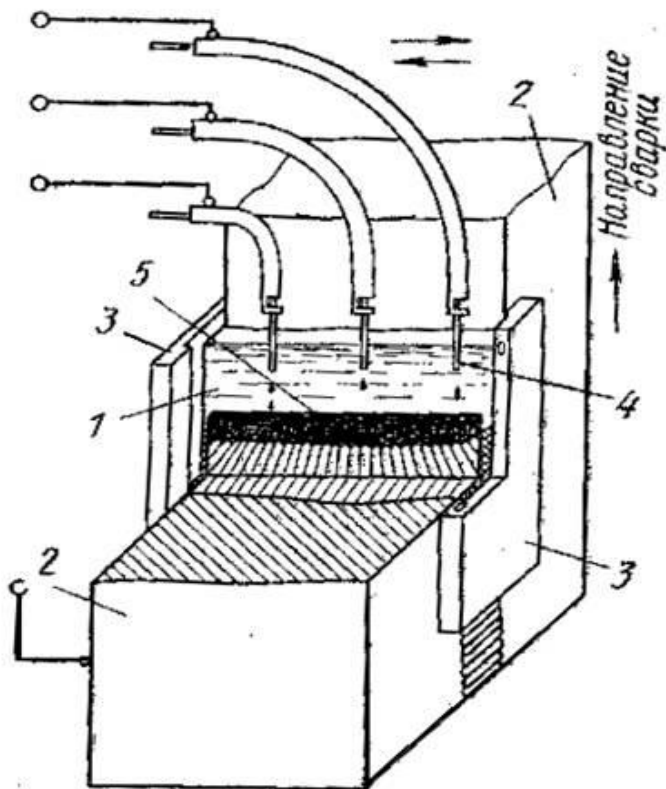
Схема электрошлаковой сварки:
